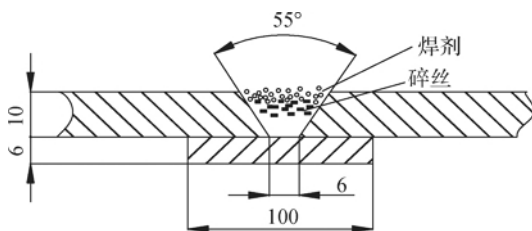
填充碎丝埋弧焊示意(单位:mm)
